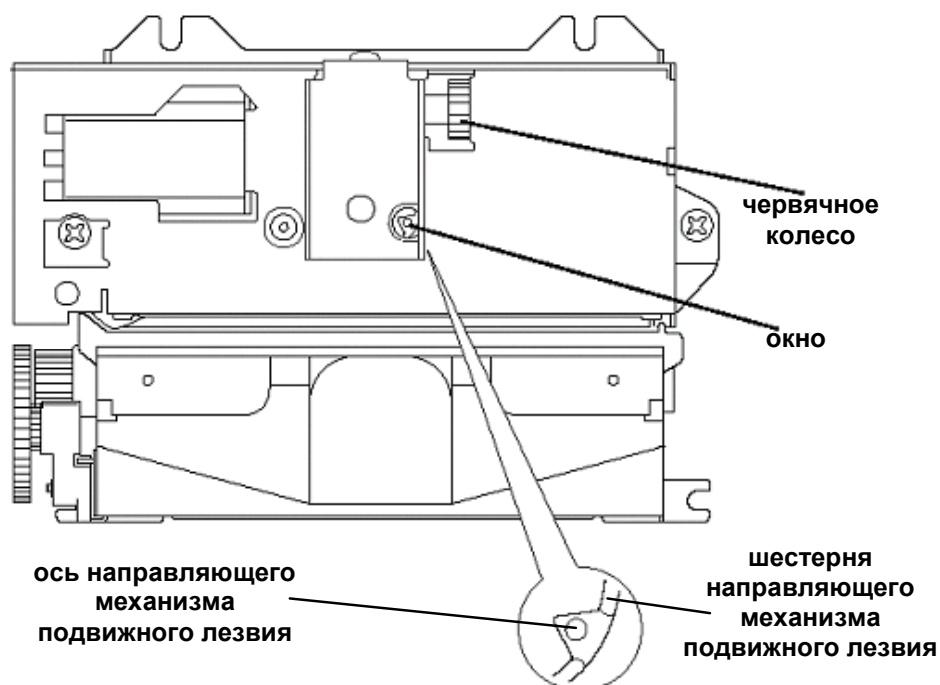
Вид механизма печати спереди (с откинутым модулем презентера)
